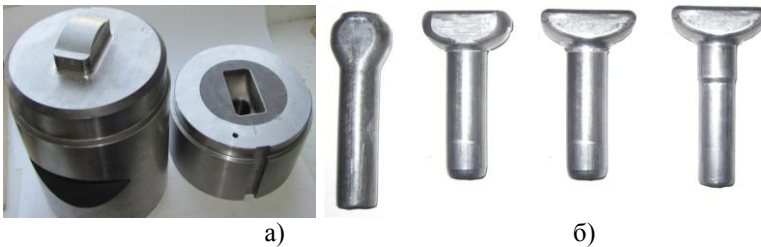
Инструмент для безоблойной штамповки (а) и заготовки по переходам разработанного технологического процесса изготовления болтов клеммных по ГОСТ 16016-79(б)
